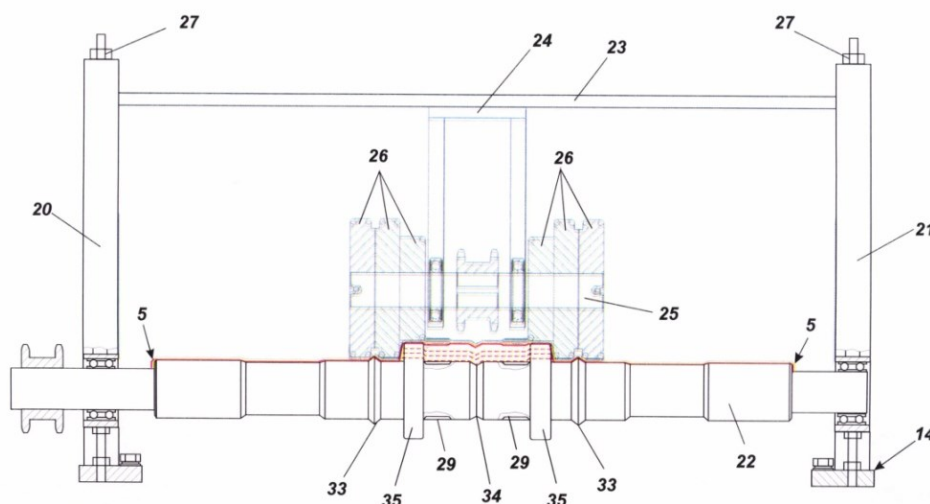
Фрагмент многоклетьевого профилегибочного стана изготовления профиля [5]:
